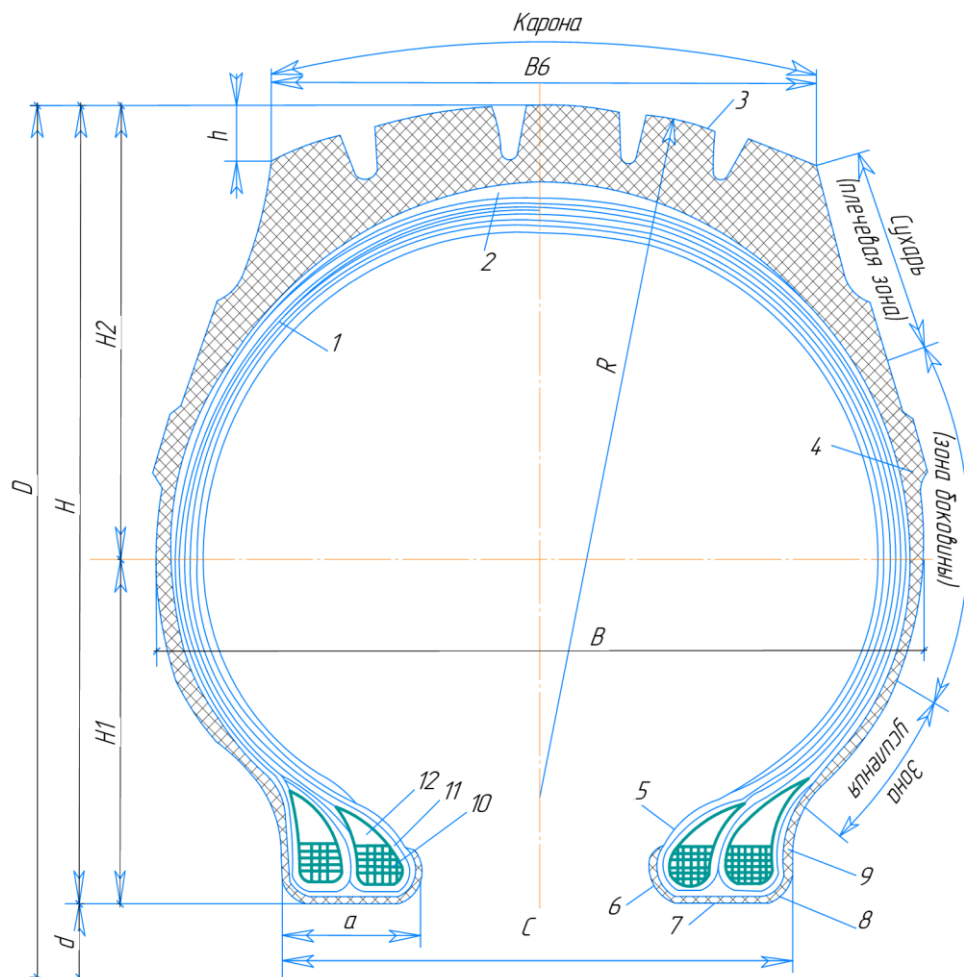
Радиальный разрез шины: 1 – каркас; 2 – подушечный слой (брекер); 3 – протектор; 4 – боковина; 5 – борт; 6 – носок борта; 7 – основание борта; 8 – пятка борта; 9 – бортовая лента; 10 – бортовая проволока; 11 – обертка; 12 – наполнительный шнур; H – высота профиля покрышки; H_1 – расстояние от основания борта до горизонтальной осевой линии профиля; H_2 – расстояние от горизонтальной оси до экватора; B – ширина профиля покрышки; B_0 – ширина беговой дорожки протектора по хорде (корона); R – радиус кривизны протектора; D – наружный диаметр шины; d – внутренний (посадочный) диаметр шины; h – стрела дуги протектора; C – ширина раствора бортов; a – ширина борта
